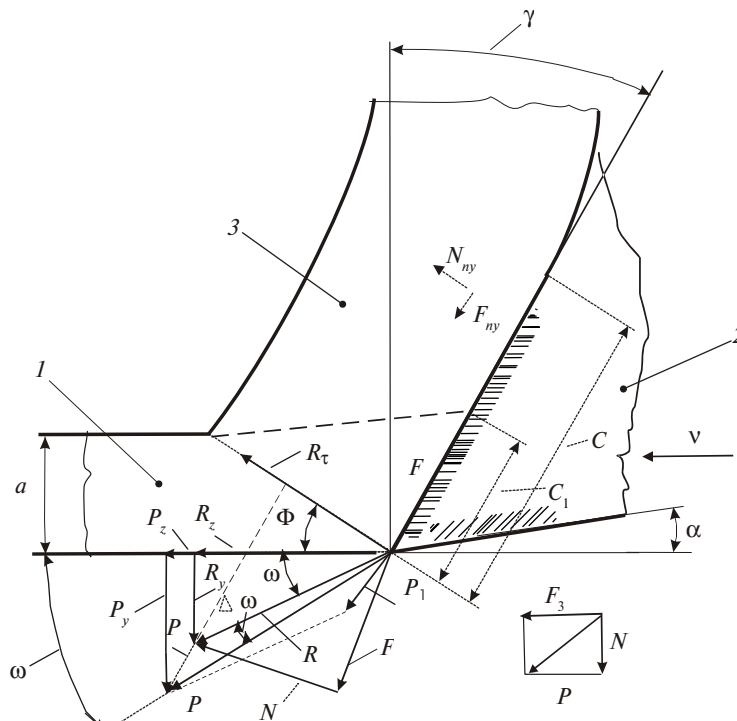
Геометрическая модель стружкообразования: 1 – образец металла; 2 – резец; 3 – стружка.
